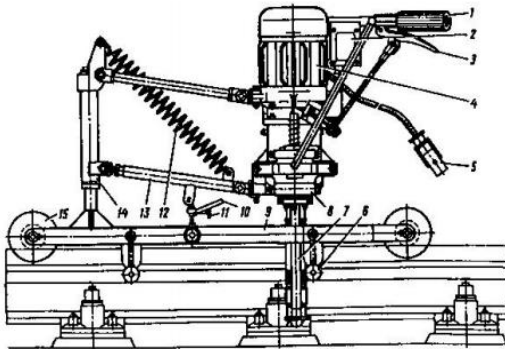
1. 6. Загальний вид шурупогайковерта ШВ2М:
